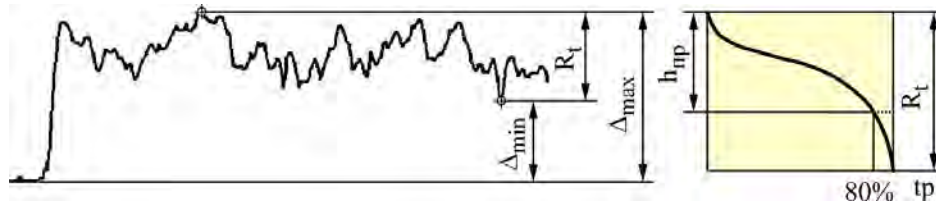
Параметры микропрофиля поверхности образца: (а) – микропрофиль поверхности; (б) – относительная опорная длина профиля.
